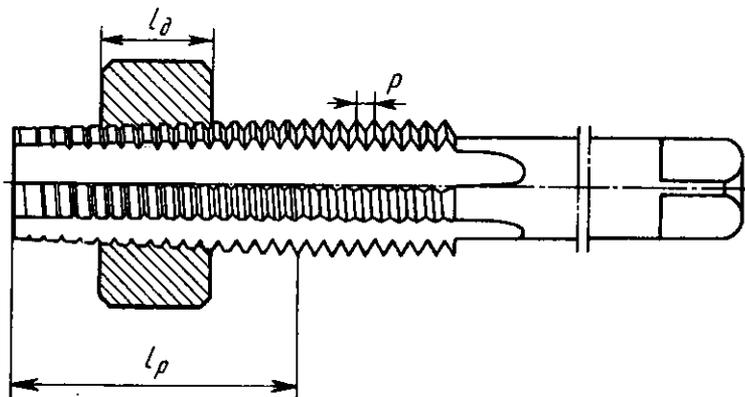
Положение нарезаемой гайки на режущей части гаечного метчика
